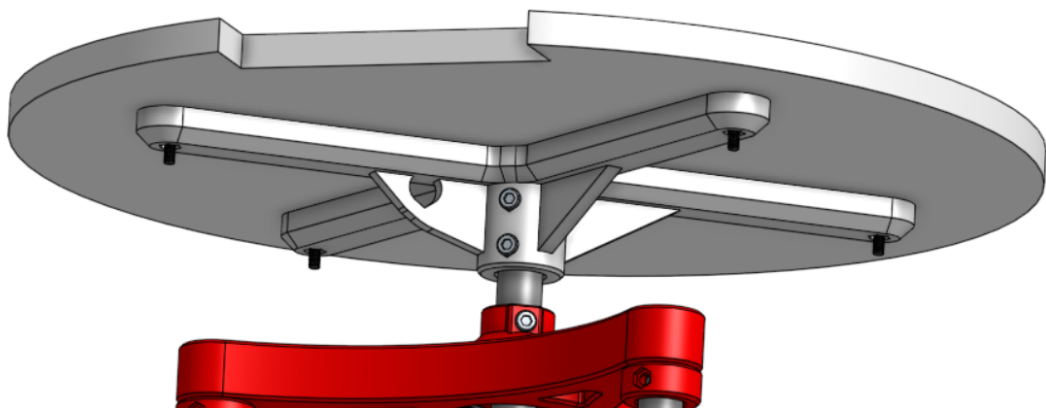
Vista isométrica 2 del ensamblaje del soporte superior con el eje principal, con el soporte de madera visible, en Onshape [fuente: elaboración propia]
